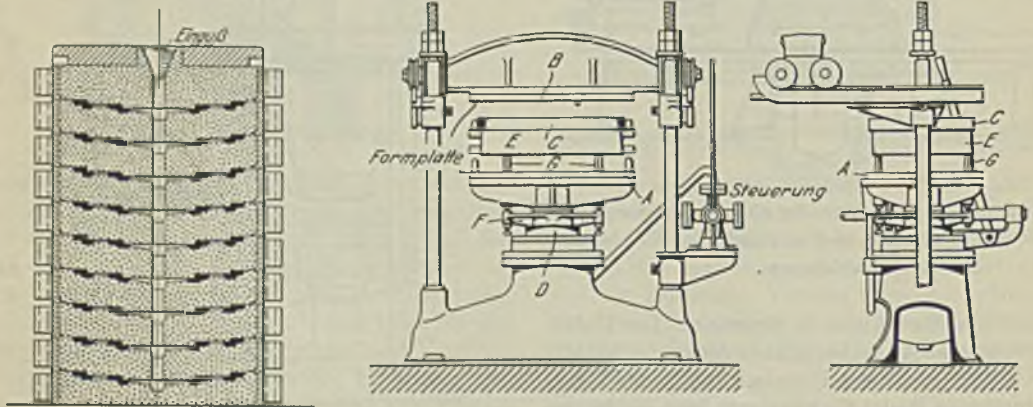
Maschine der Badischen Maschinenfabrik für doppelseitige Pressung.
